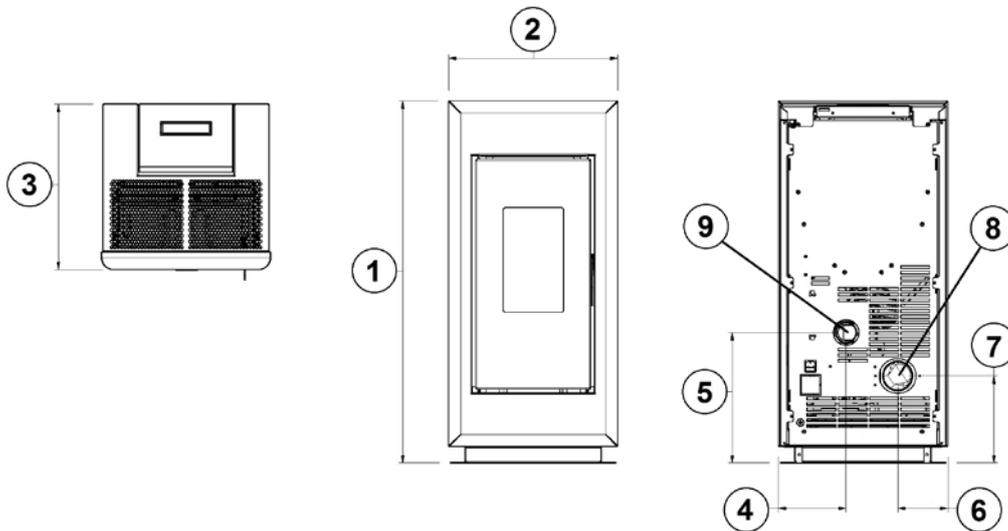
Γενικές διαστάσεις: ACCENT AIRTIGHT
